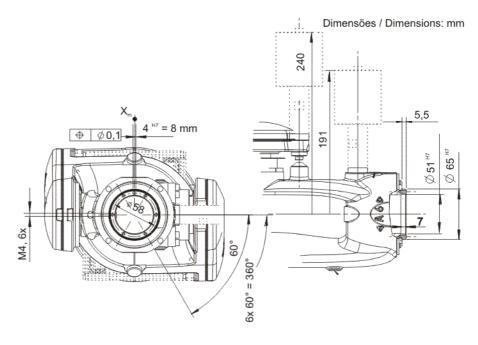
Flange de fixação KR 16 L8 arc HW
